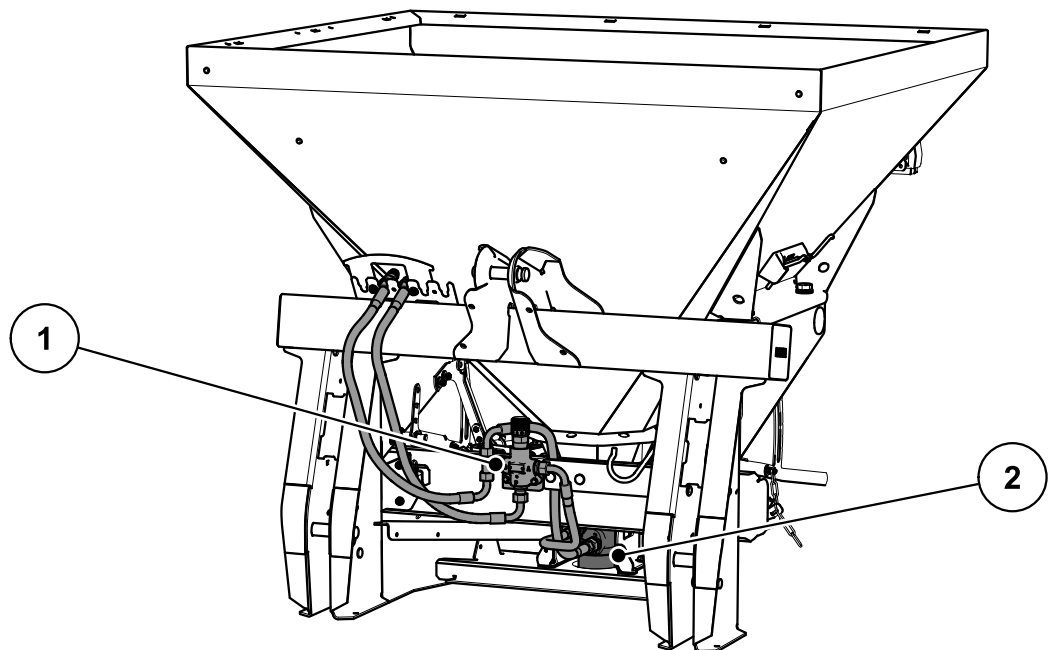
Komponentgruppöversikt: Hydraulisk drivenhet
